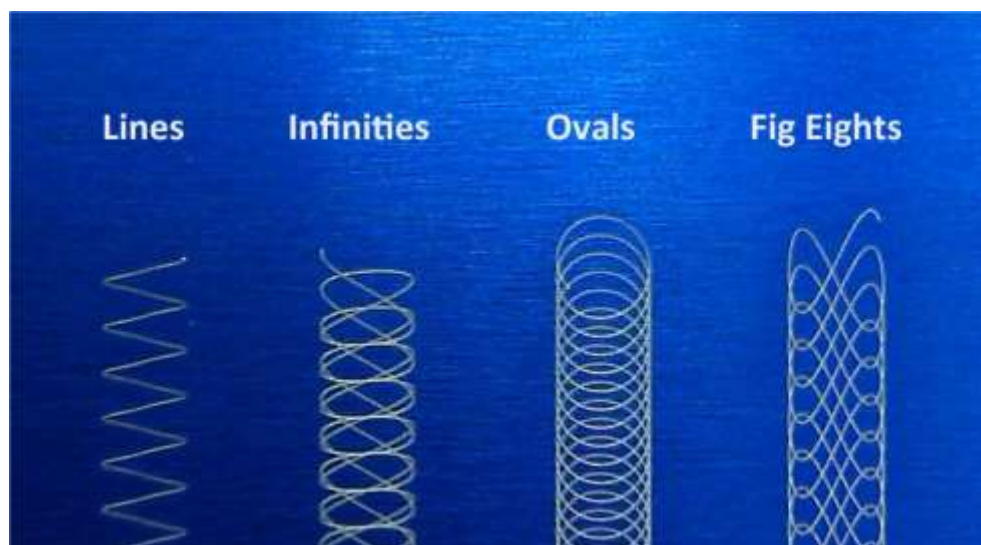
Примеры траекторий движения фокусного пятна при лазерной сварке с осцилляцией фокусного пятна (англ., Laser Wobble Welding) © Polaris Laser Wobble Technology.
